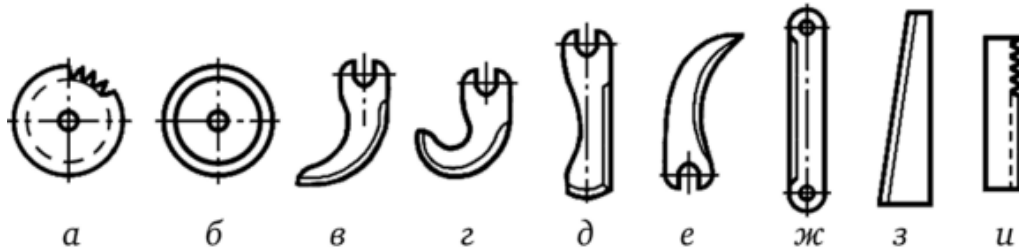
Форми ножів: а — зубчастий дисковий; б — гладкий дисковий; в—е — серповидні; ж, з — гладкі пластинчасті; и — зубчасті пластинчасті
